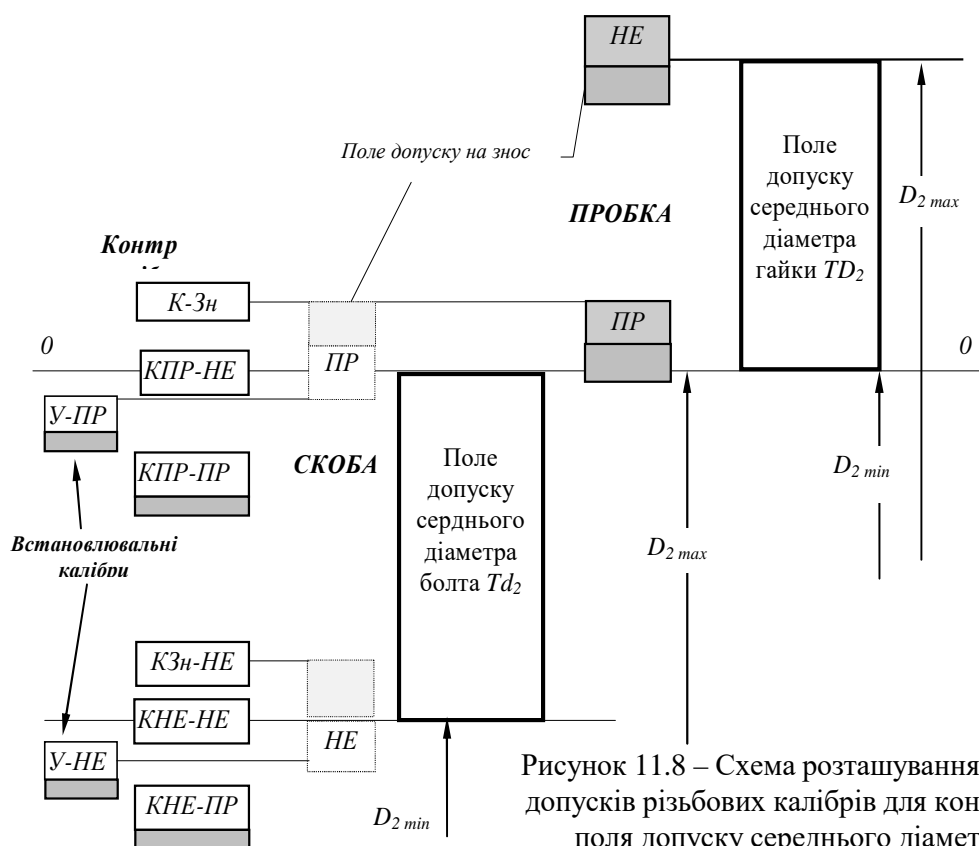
Схема розташування полів допусків різбових калібрів для контролю поля допуску середнього діаметру
